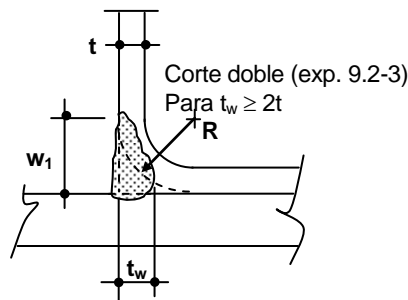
Soldadura a tope acampanada en bisel (Filete enrasado con superficie $w_1 = R$)
